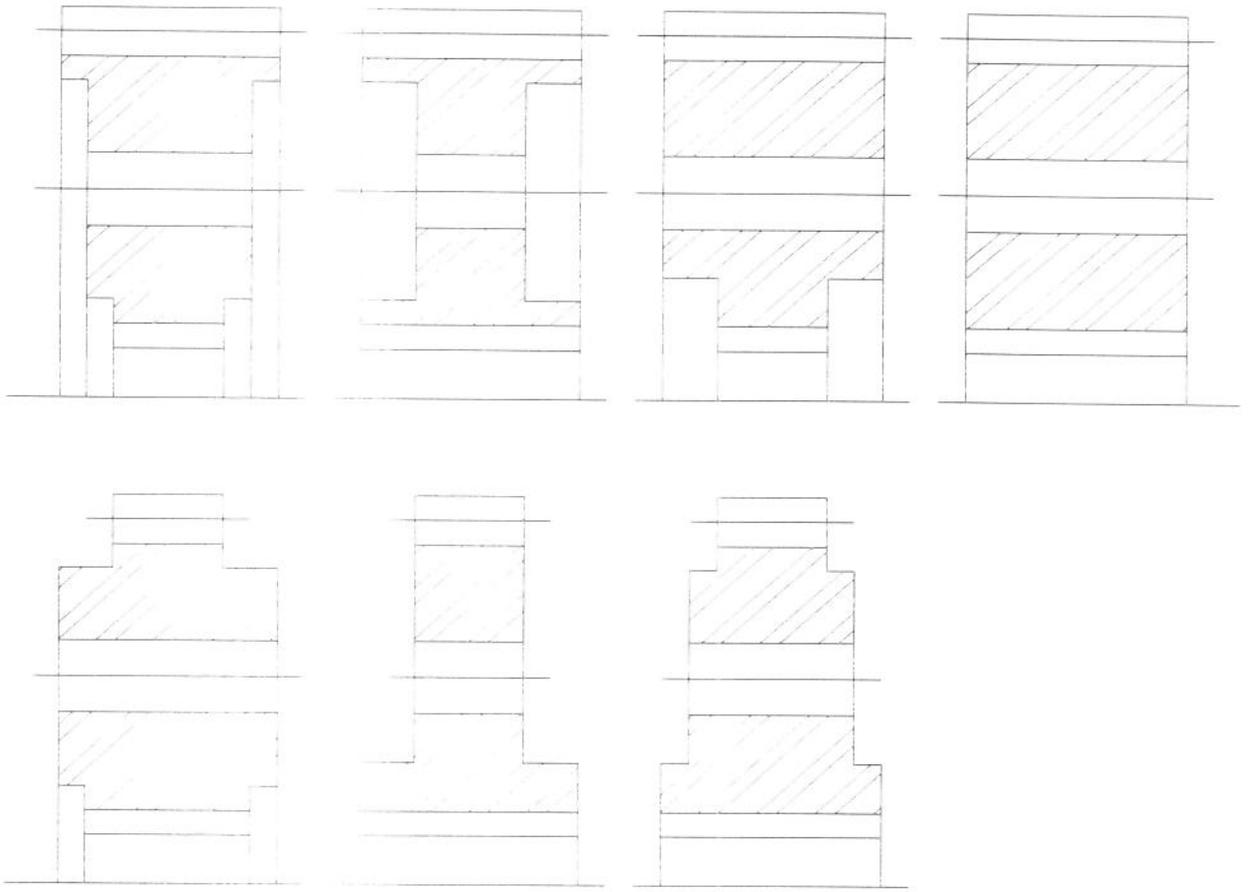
Variações do corte transversal da engrenagem com furo na alma e chaveta
